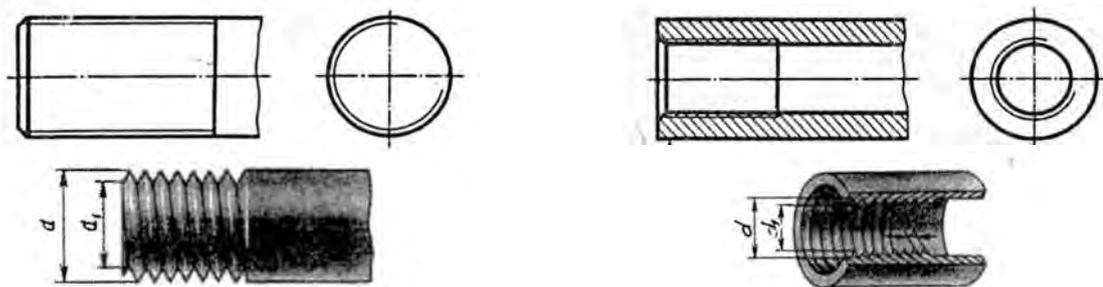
Изображение резьбы на цилиндрических поверхностях
